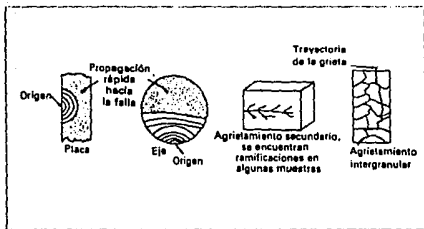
Agrietamiento por esfuerzo.(19)
